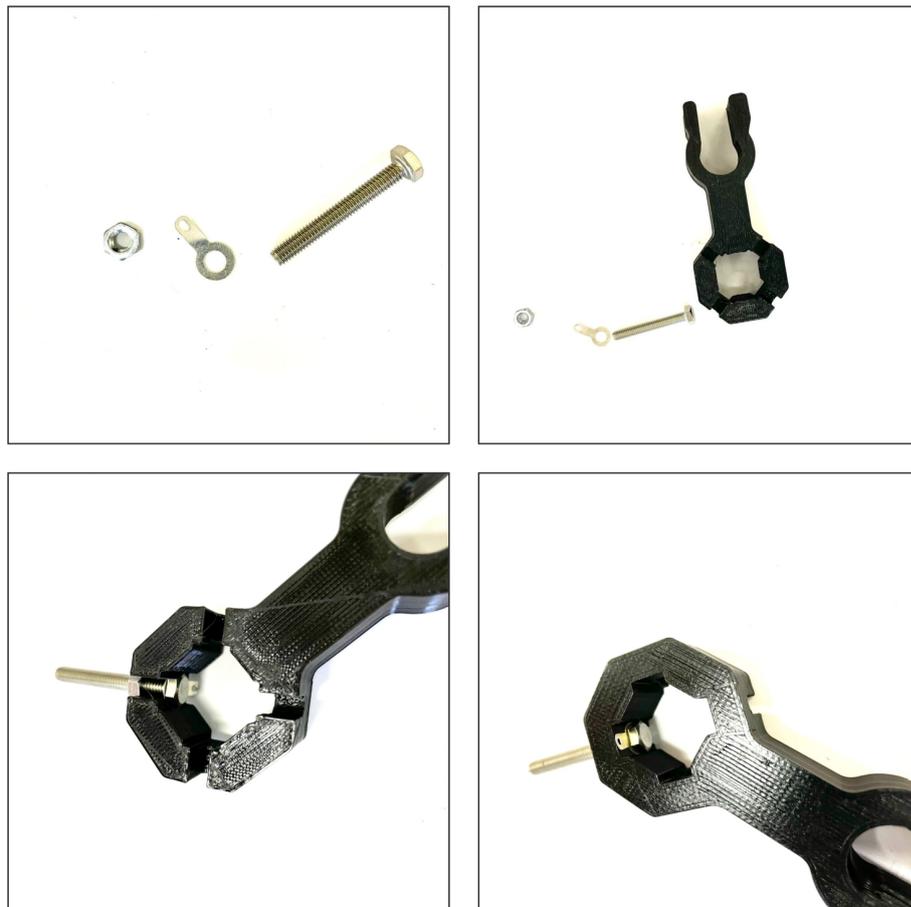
Крепление винтов с контактными лепестками (фото)
